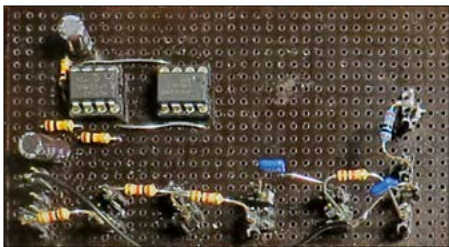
Versuchsaufbau der Gyratorschaltung mit Steckbrücken für Z_0 bis Z_5 auf einer Lochrasterplatte
